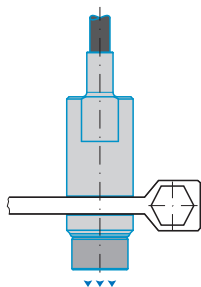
Geschirmter Sensor mit Gewinde in Standardmontage
